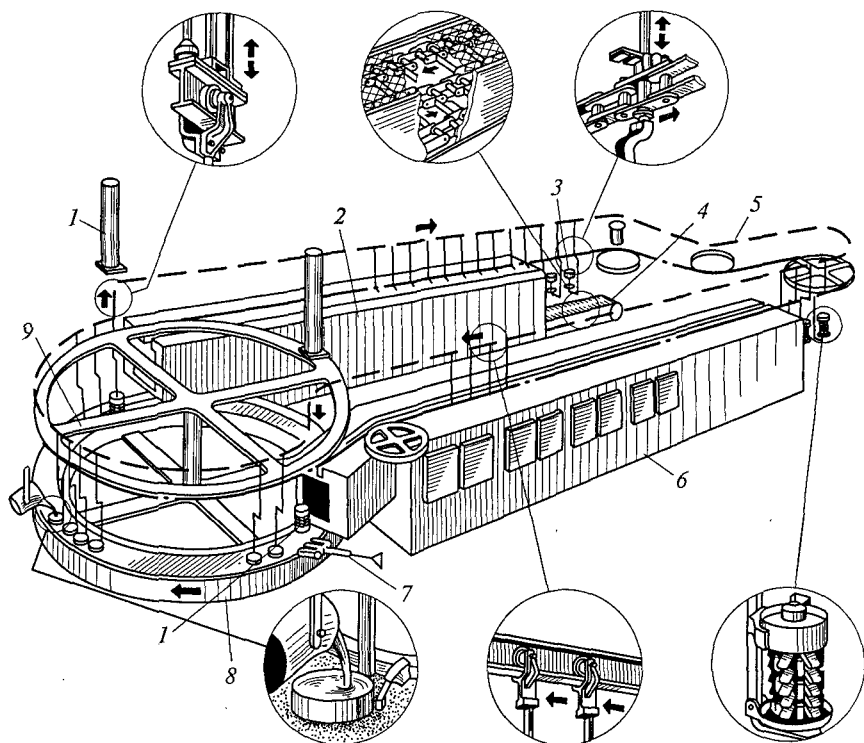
Схема агрегата для прокаливания, формовки, заливки и выбивки оболочковых форм:
